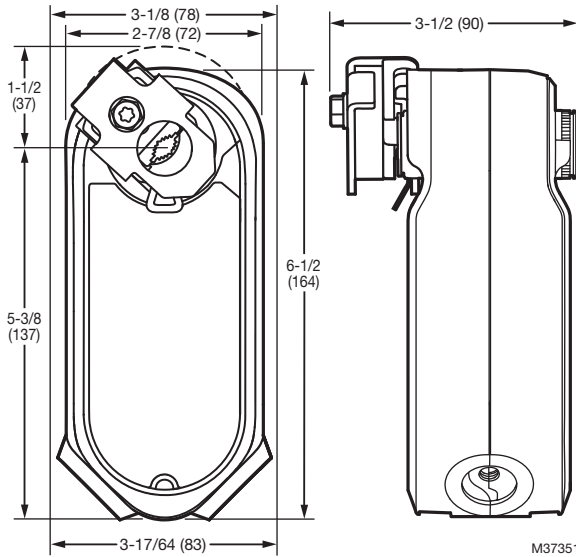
Aktüatörün inç (mm) cinsinden boyutsal çizimi. A ve B boyutları için Tablo 2'ye bakınız.
